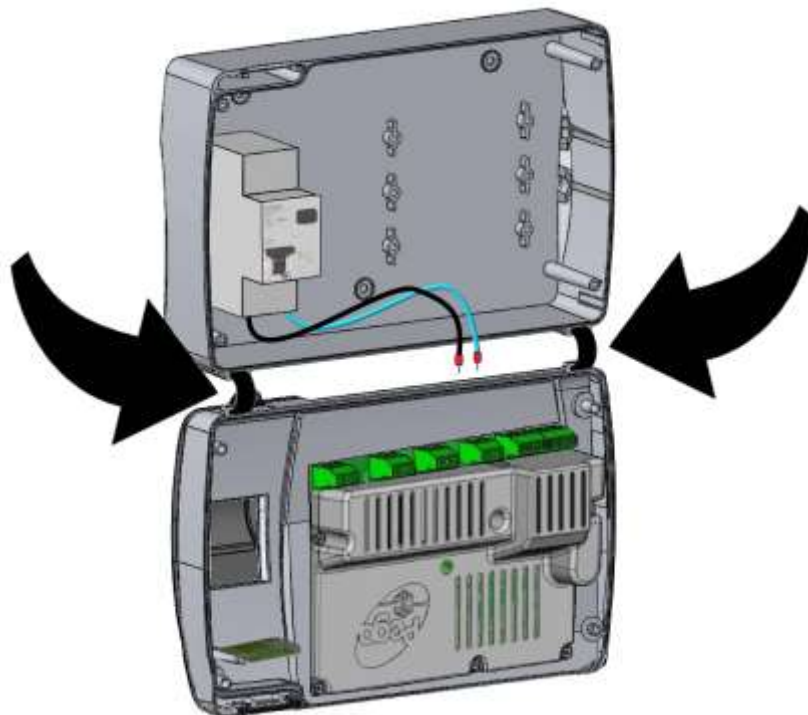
Einen Druck seitlich jedes einzelnen Scharniers ausüben, um es aus seiner Aufnahme herauszuziehen und das Vorderteil vollständig entfernen. Press on the sides of the hinges to remove them from their seats and so remove the front panel completely.
